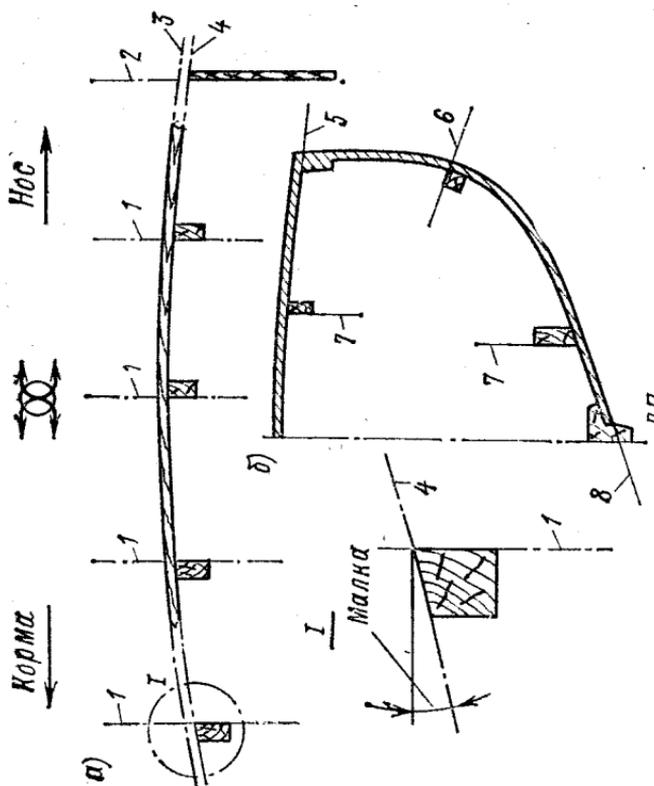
Положение теоретических линий конструктивных элементов корпуса: а — план корпуса; б — поперечное сечение.
